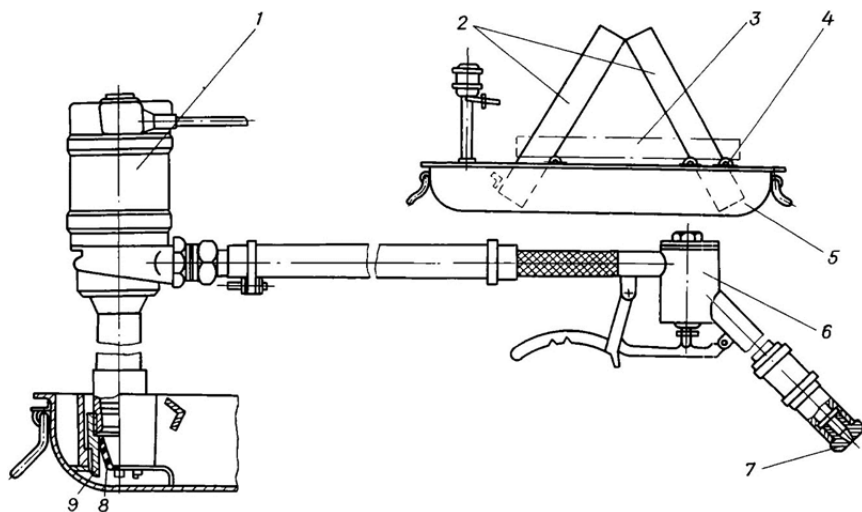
Приспособление для промывки кассет воздухоочистителя:
